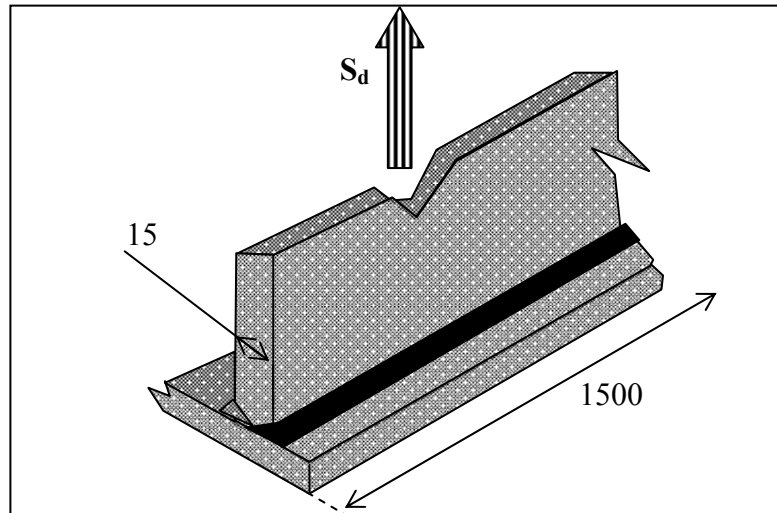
Section soudée sollicitée à la traction
